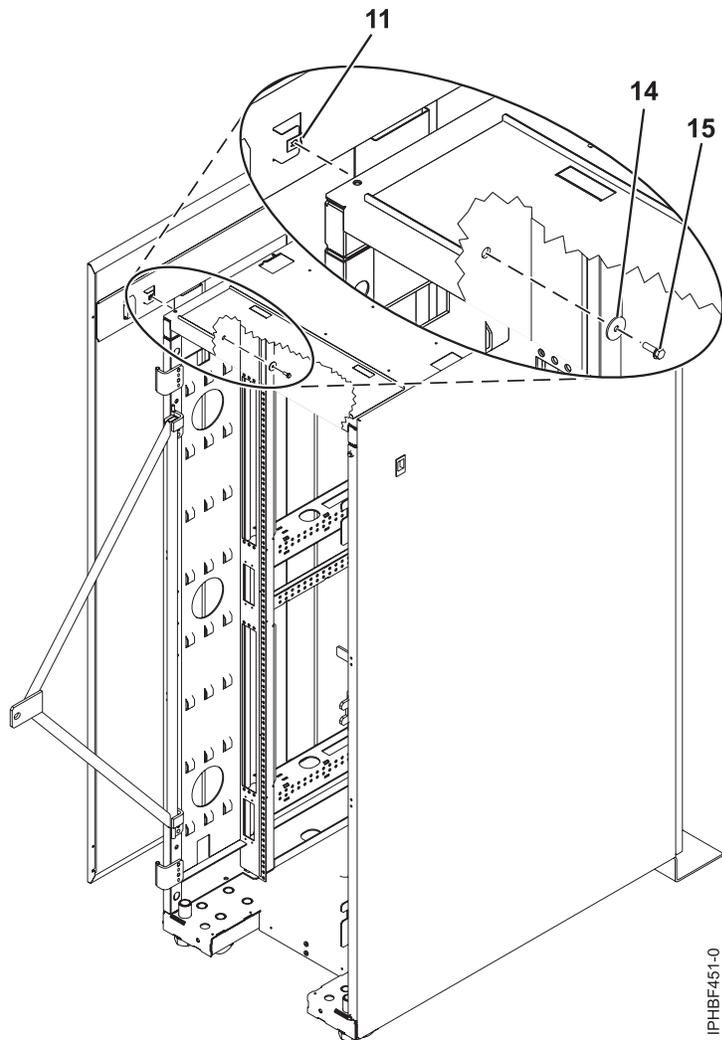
Befestigungsschrauben an Seitenabdeckung entfernen
